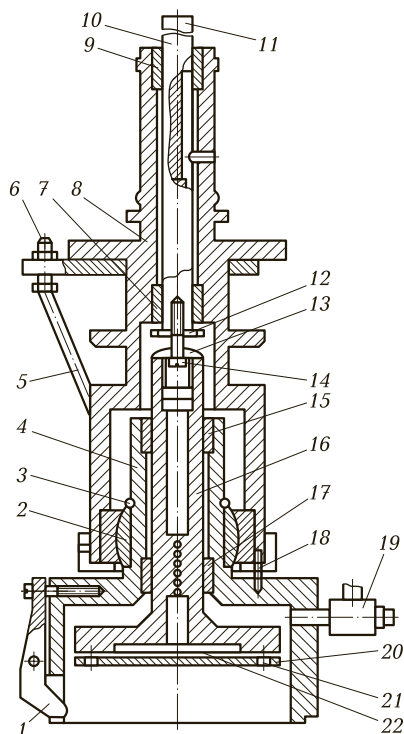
Инструмент для захвата и монтажа подшипника качения в отверстие базовой детали:
